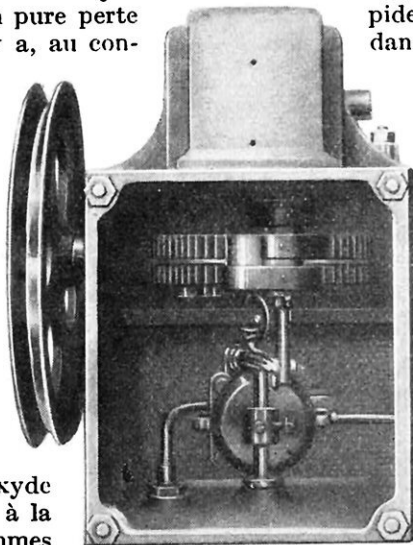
RÉGULATEUR AUTOMATIQUE, LE COUVERCLE ENLEVÉ
